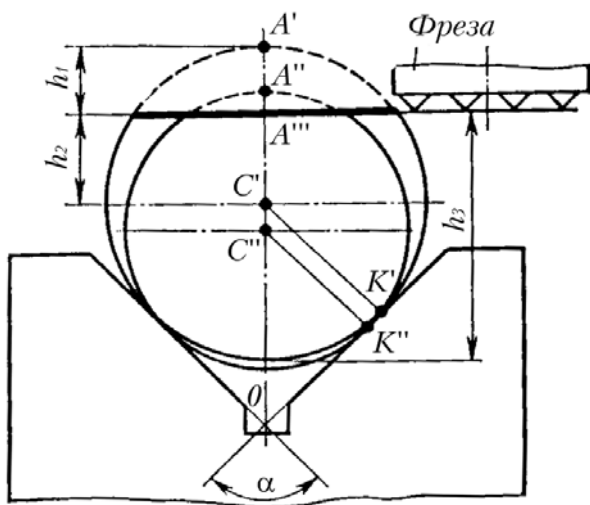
Розрахункова схема для визначення похибок базування при встановленні на призму.
